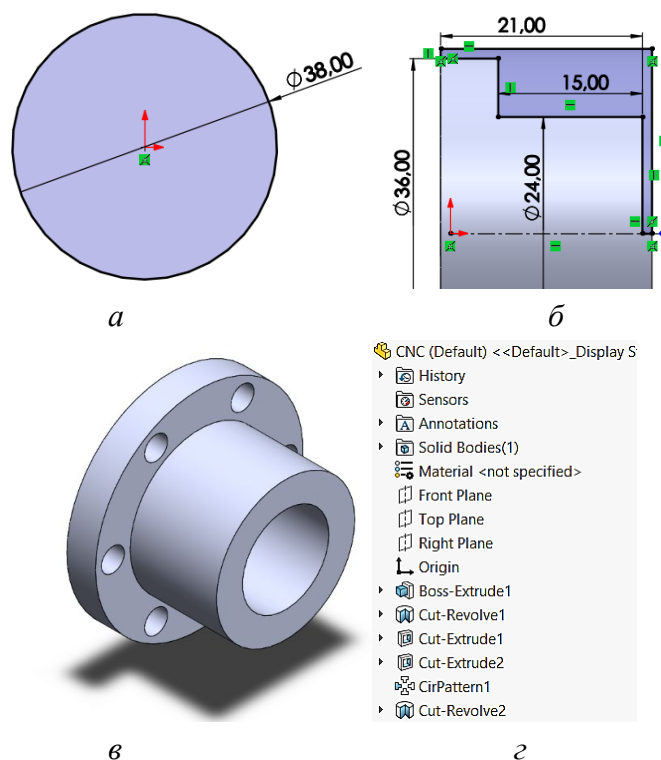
Просторова модель втулки для виготовлення на верстаті з ЧПК:
